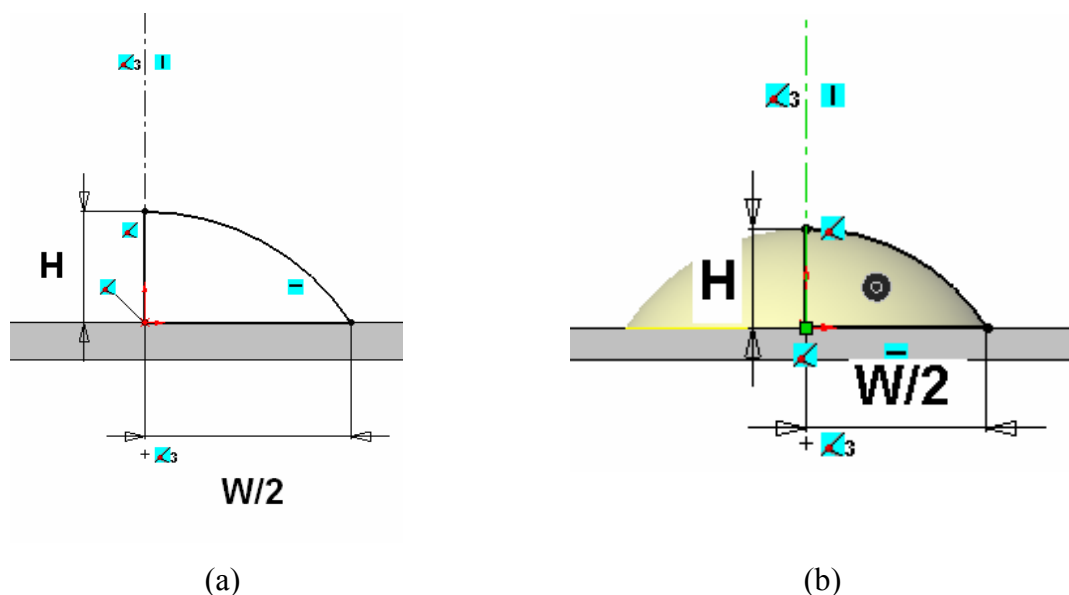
(a) Arco de circunferência desenhado utilizando a largura e a altura do cordão de solda. (b) Revolução do arco para formar da seção do cordão de solda.
